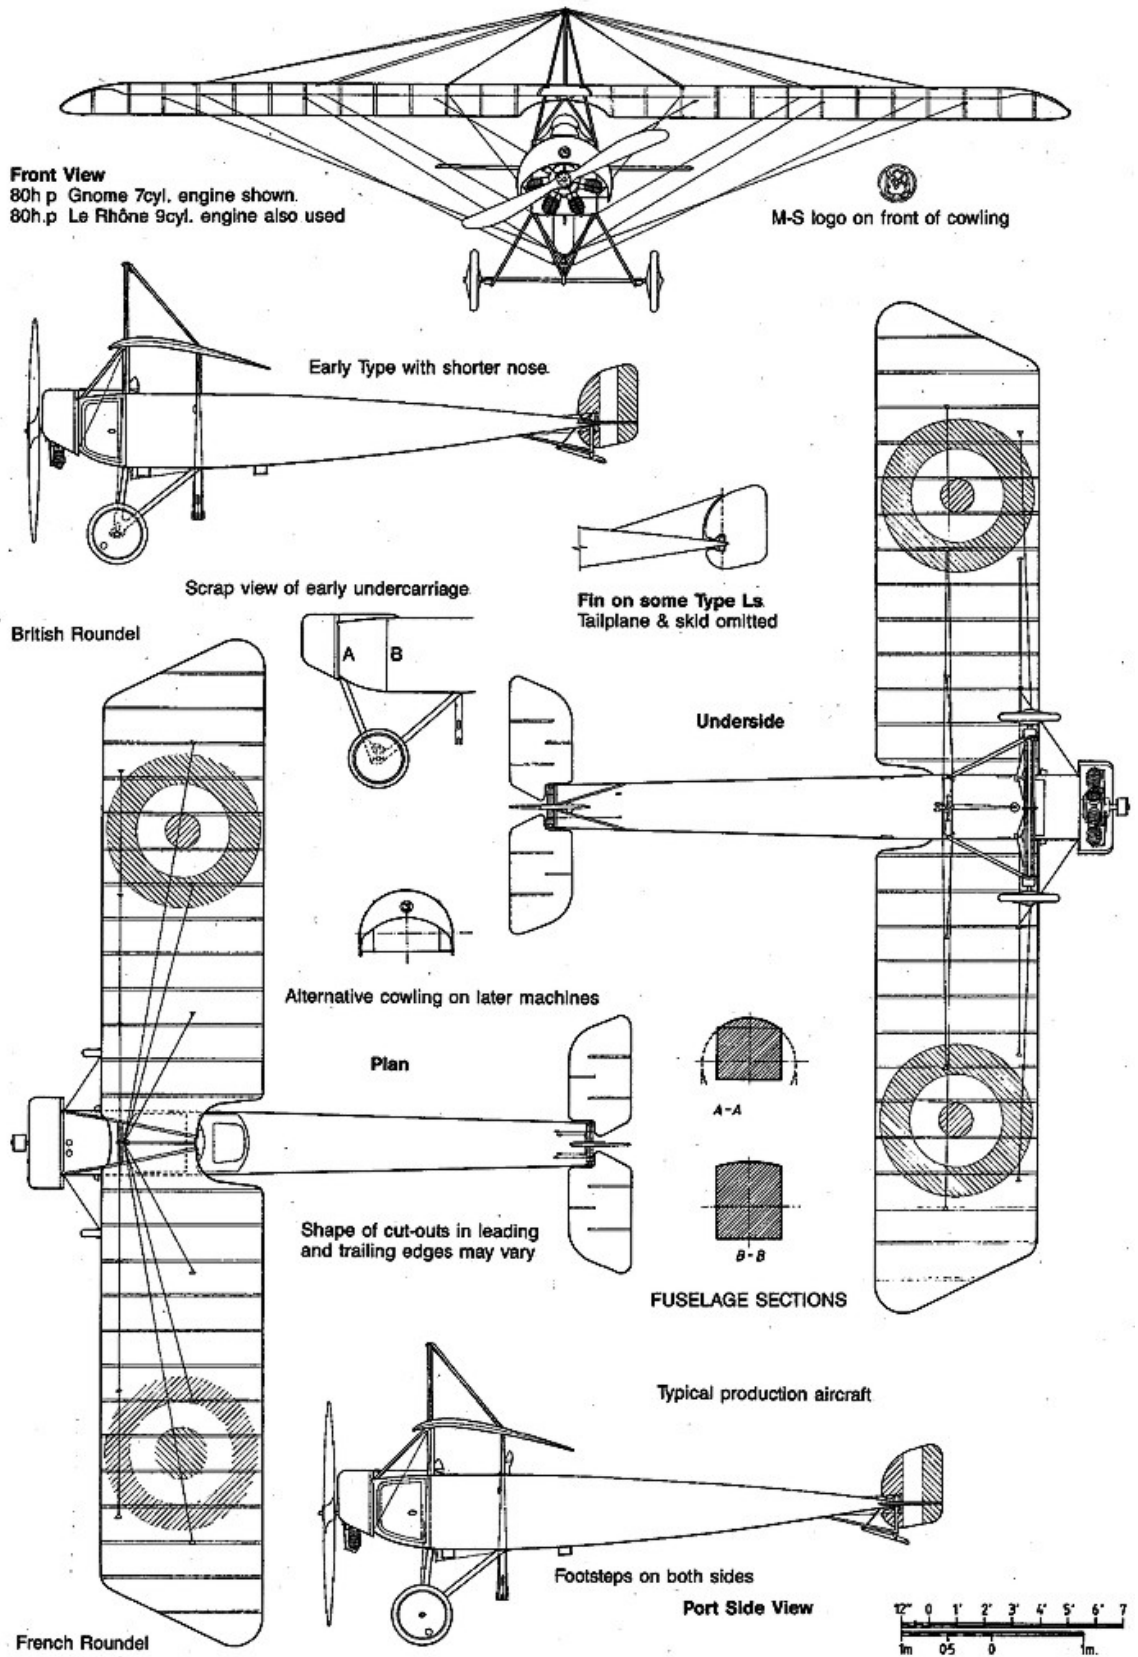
Planta da aeronave Morane-Saulnier tipo L (Parasol) ,
